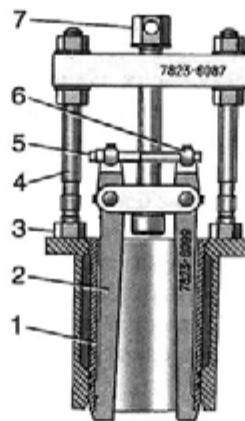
Выпрессовка гильзы из блока цилиндров комбинированным съемником:
